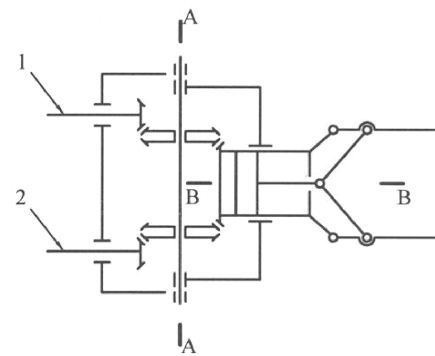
Typy konstrukce orientačního ústrojí
